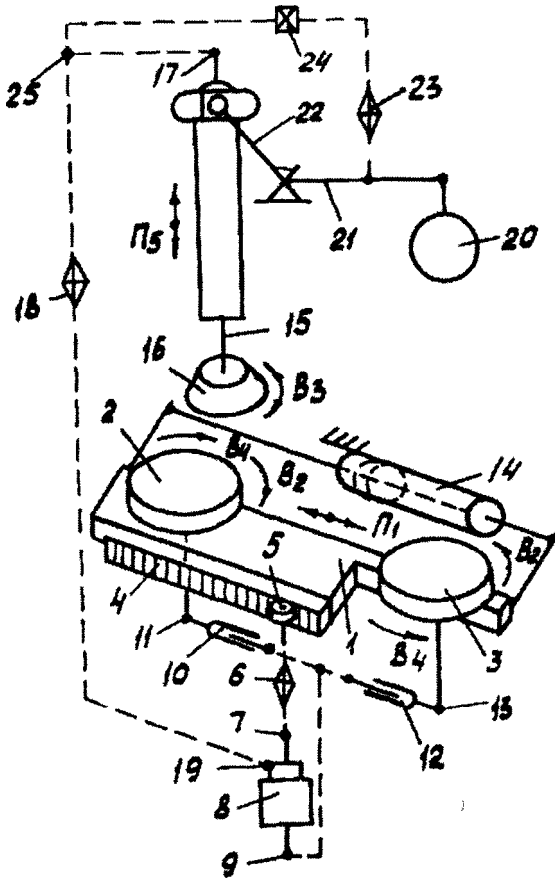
Кинематико-компоновочная схема станка для последовательной обработки зубчатых колес
